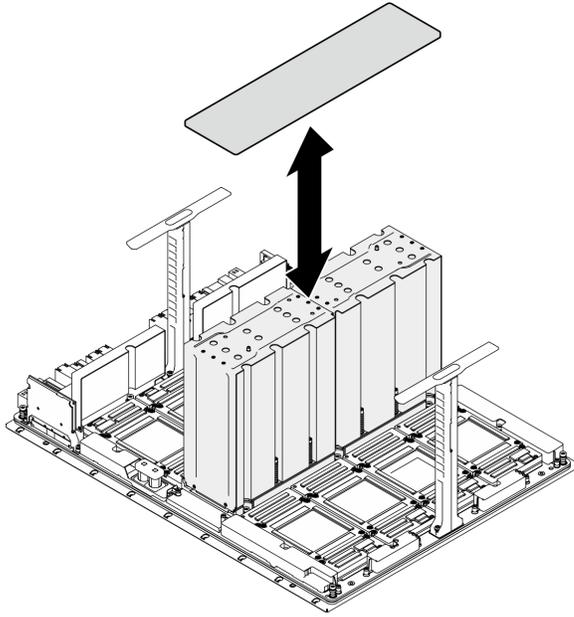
Remoção da tampa do dissipador de calor NVSwitch
